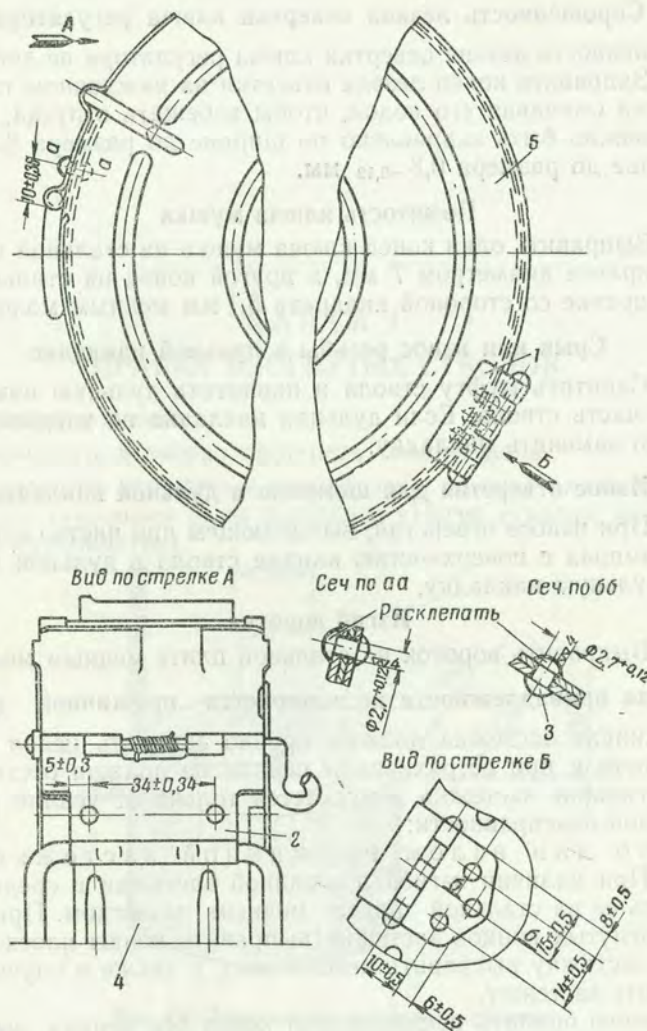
Приклепка петли крышки коробки и петли ручки и запора:
